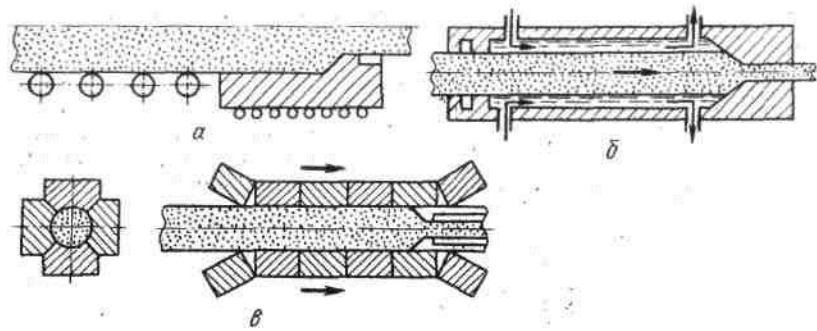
Схеми безперервного пресування при подачі заготовки:
